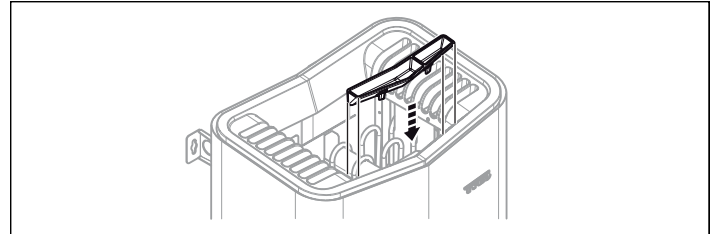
Установка контейнера для ароматизатора/увлажнителя воздуха
